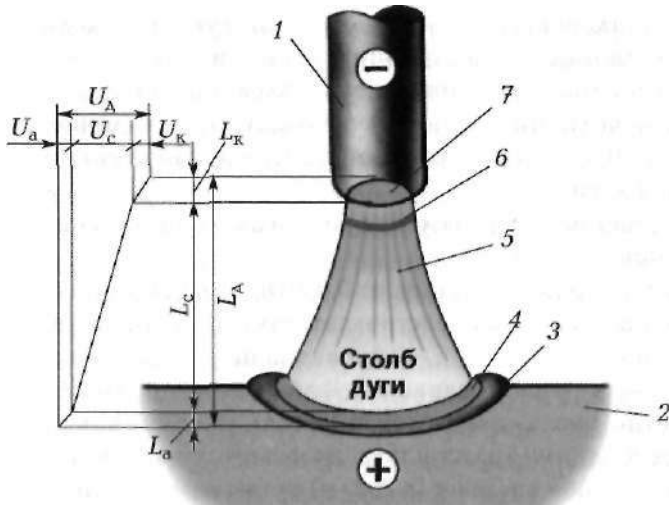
Схема сварочной дуги и падения напряжения в ней:
